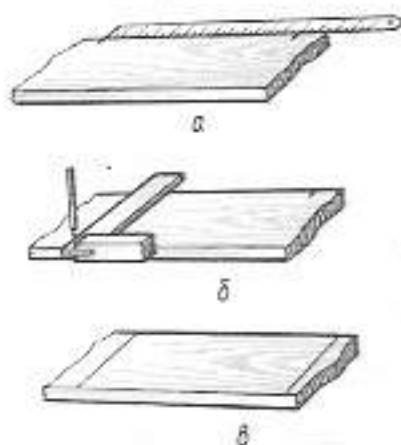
Разметка стенок ящика: а — разметка длины деталей; б — нанесение линии по угольнику; в — размеченная заготовка.
